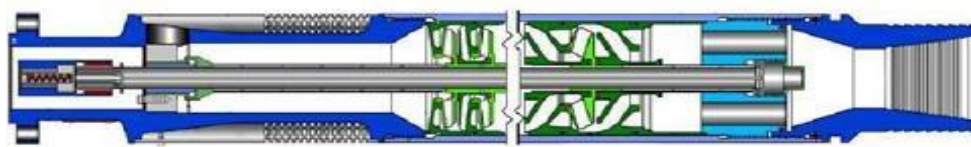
Центробежный газосепаратор фирмы Centrilift
